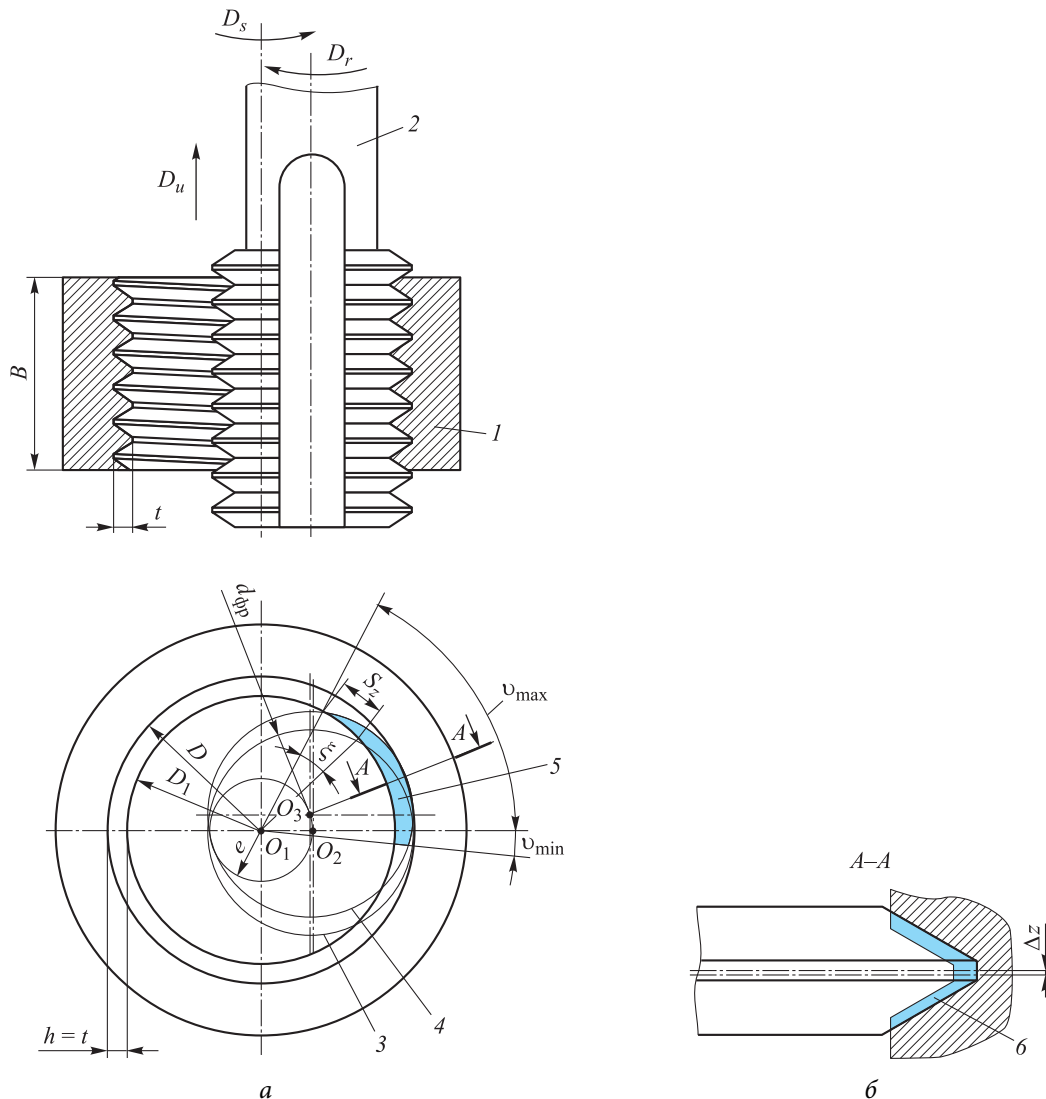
Схема формирования срезаемого слоя (а) и смещения инструмента вдоль оси (б): 1 — заготовка; 2 — резьбовая гребенчатая фреза; 3 — начальное положение резьбовой фрезы; 4 — положение резьбовой фрезы, соответствующее повороту на один угловой шаг; 5 — срезаемый слой; б — ССС; t — глубина резьбофрезерования; h — высота профиля резьбы; B — ширина резьбофрезерования
